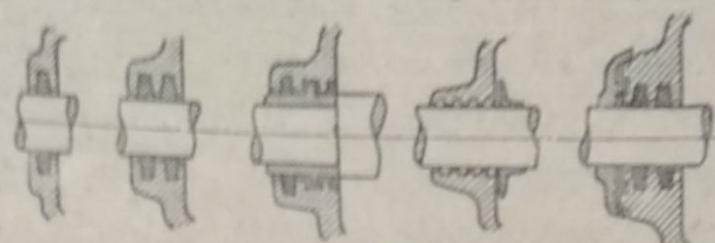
Типы уплотнения корпуса шарикоподшипников:
